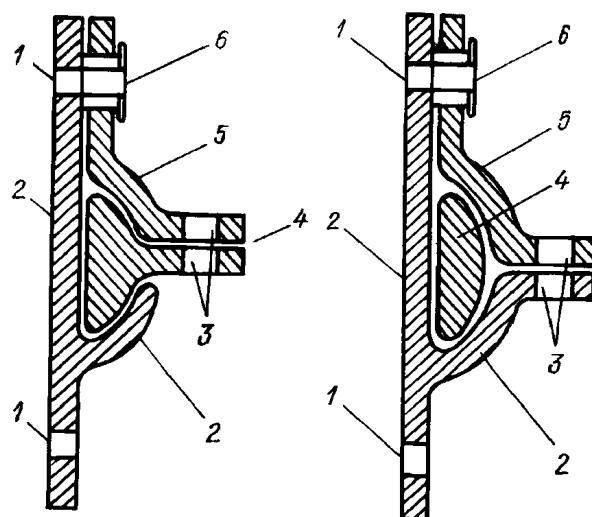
Приспособления для наложения таможенных печатей и пломб:
